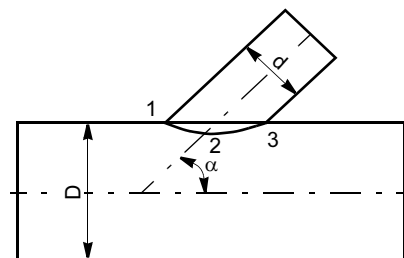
Формирование сварного шва в узлах конструкций из труб
